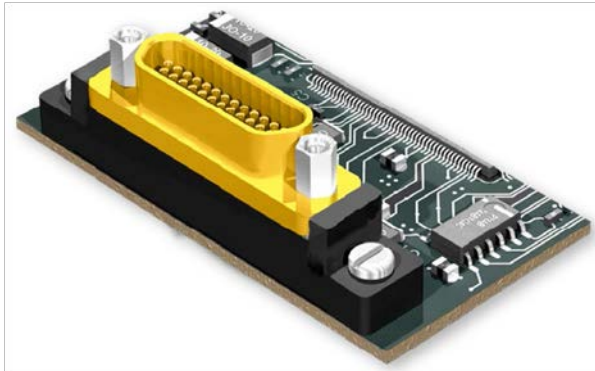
Θηλυκοί PCB Mounting Connectors με ευθύ σχήμα (Micro-D GMR7580C Compact Flange Vertical Mount PCB Connectors) [40].
